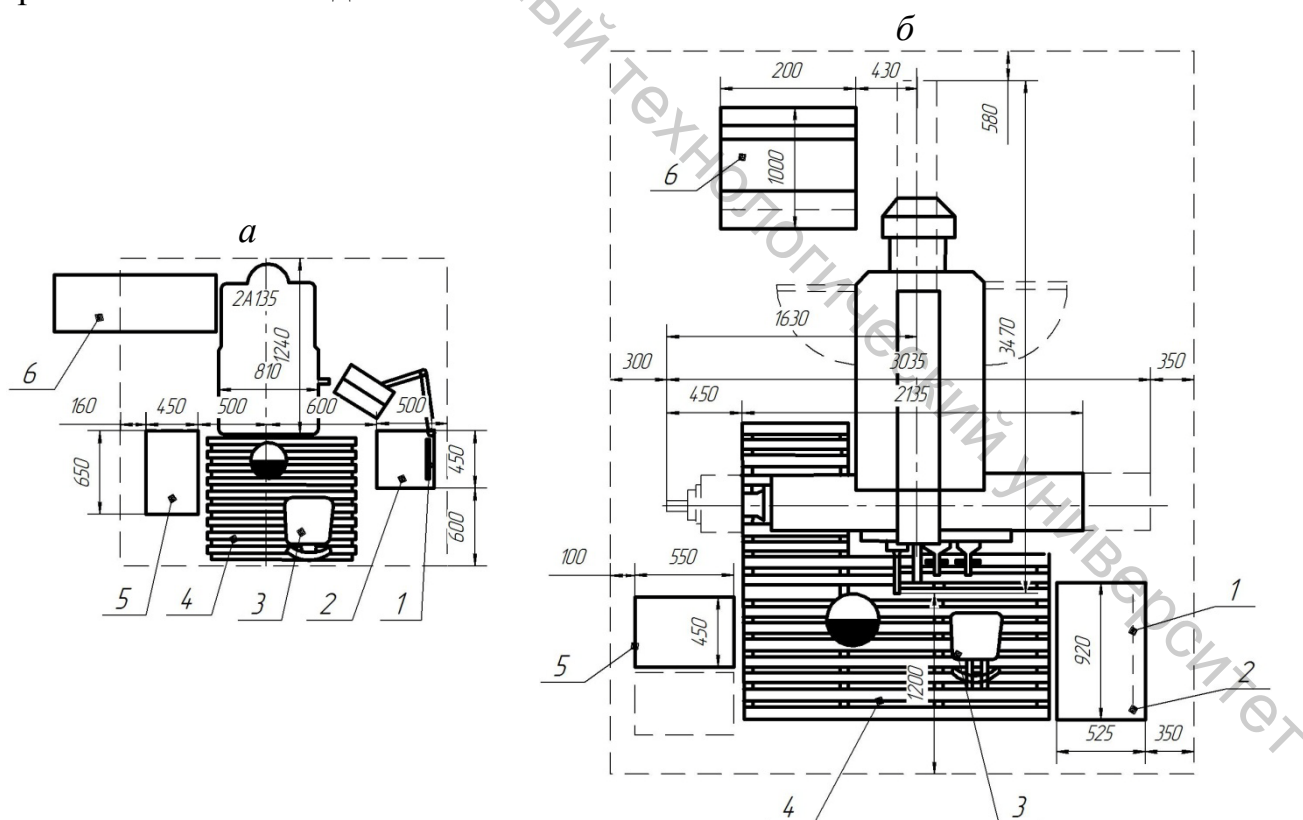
Планировка рабочих мест сверловщика (а) и фрезеровщика (б):
